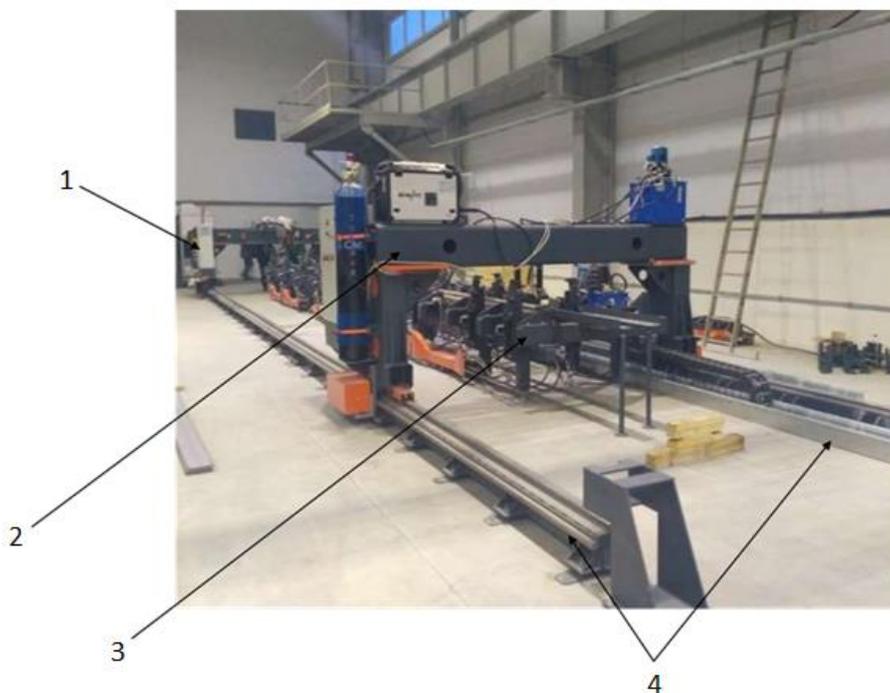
Общий вид комплекса АКСЛ-3, где 1- сварочный портал, 2 – сборочный портал, 3 – стапель для сборки-сварки лонжеронов, 4 – направляющие рельсы.
